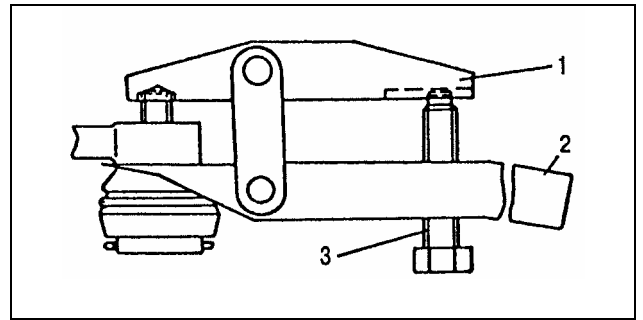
Выпрессовка пальца шарового шарнира из поворотных рычагов и бобышек тяги сошки съемником:
